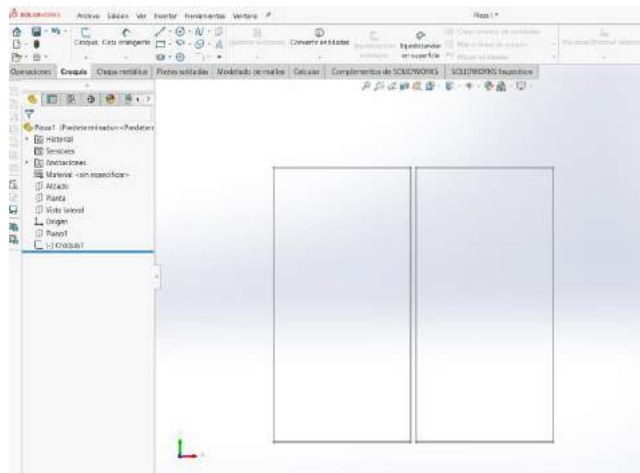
Croquis de las planchas de acero ASTM A-500
